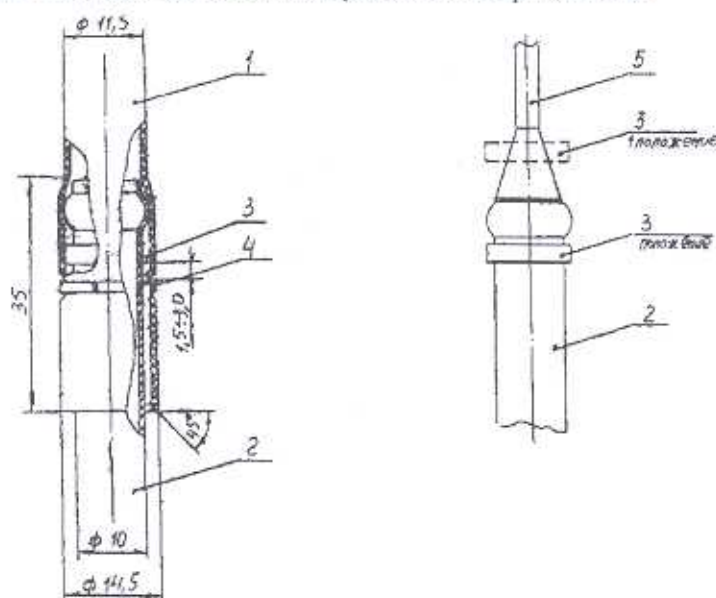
Крепление фторопластовой трубки на штуцере охладителя сердечника статора:
